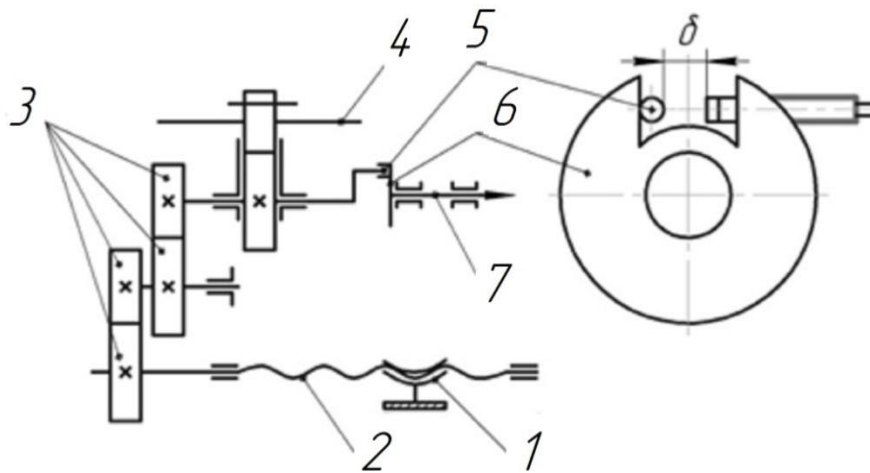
Схема компенсации зазора в передачах механизма подачи резьбошлифовального станка
